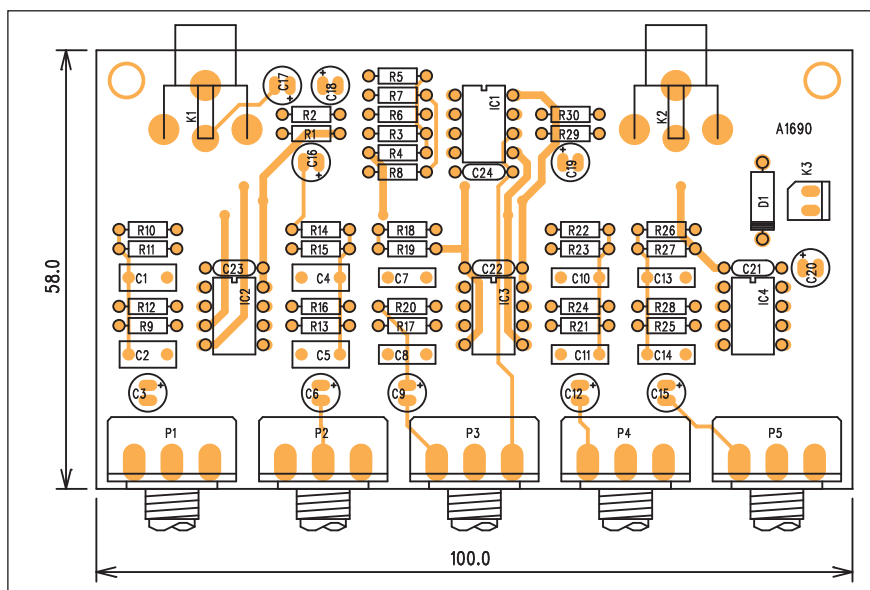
Obrazec desky spojů crossoveru (strana BOTTOM)
